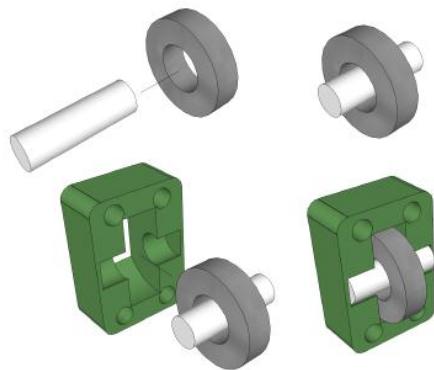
Ensamblado del cuerpo del extrusor (paso 2)
